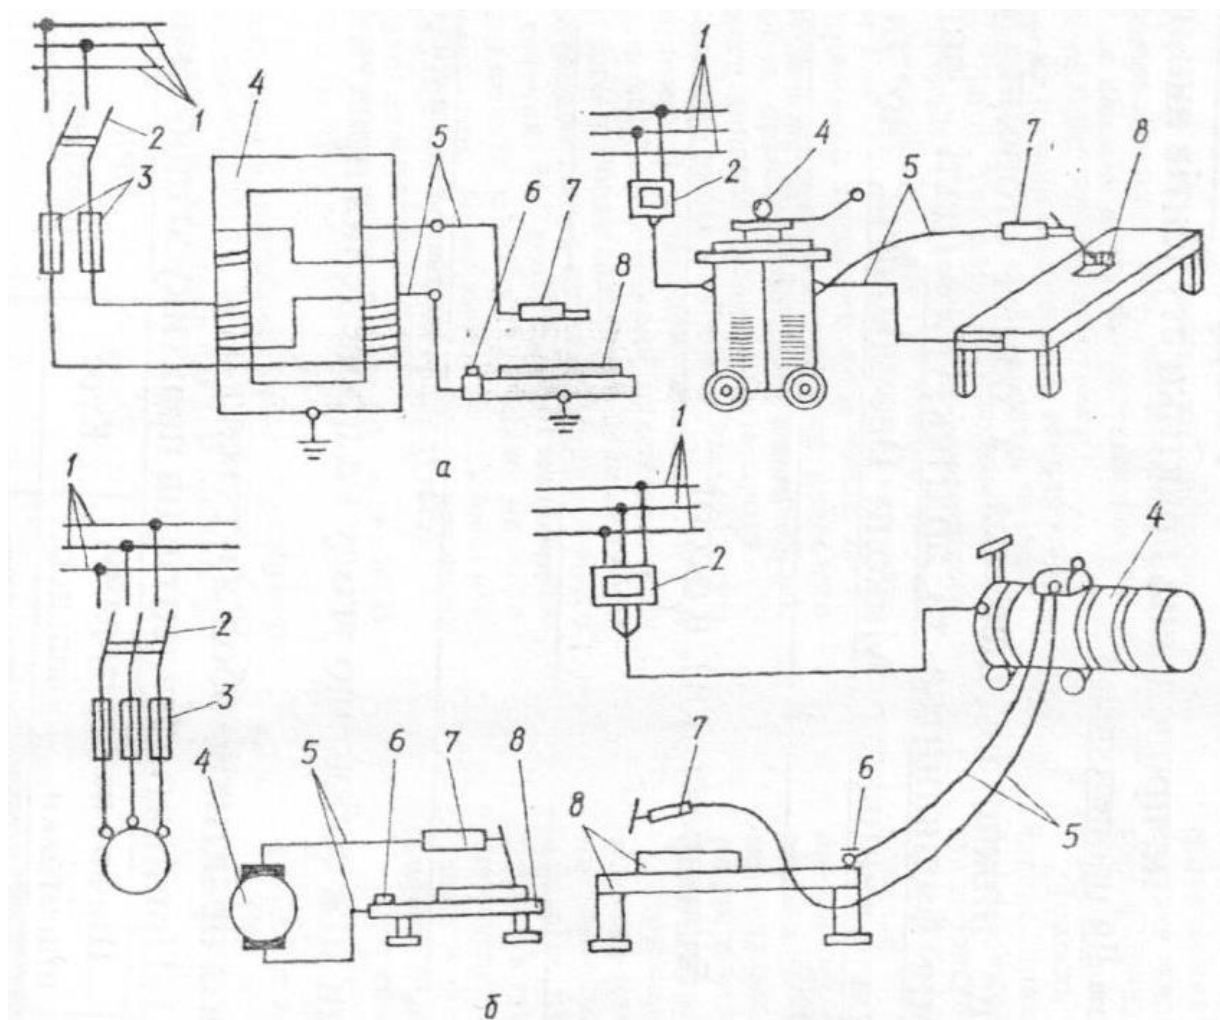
Зварювальний пост для ручного зварювання: а – змінним струмом; б – постійним струмом; 1 – мережа змінного струму; 2 – рубильник; 3 – запобіжник; 4 – зварювальний трансформатор; 5 – зварювальні дроти; 6 – затискач; 7 – електроутримувачі; 8 – виріб.
